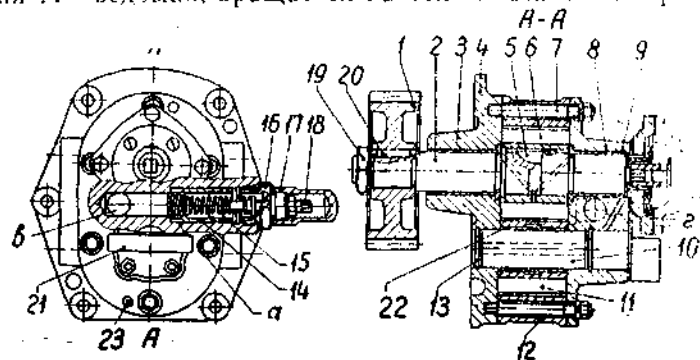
Циркуляционный масляный насос: 1—шестерня; 2—приводной валик; 3—втулка; 4—крышка; 5—сегментная шпонка; 6—ведущая шестерня; 7—шпилька; 8—крышка; 9—втулка; 10—ось; 11—ведомая шестерня; 12—корпус; 13—стопорное кольцо; 14—клапан; 15—пружина; 16—штуцер; 17—колпак; 18—винт; 19—гайка; 20—шпонка; 21—перепускной клапан топлива; 22—втулка; 23—штифт
